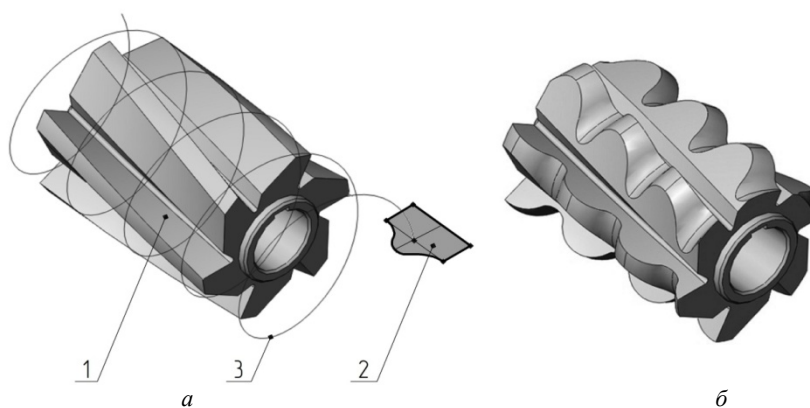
Формоутворення черв'ячної фрези в CAD – системі Solid Works
